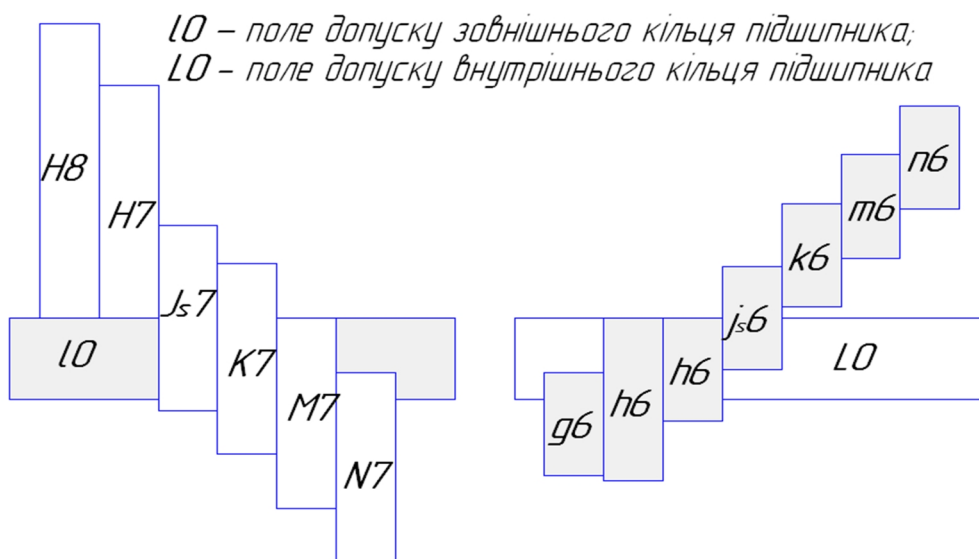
Розташування полів допусків приєднувальних поверхонь при монтажі підшипника 0-го класу точності
